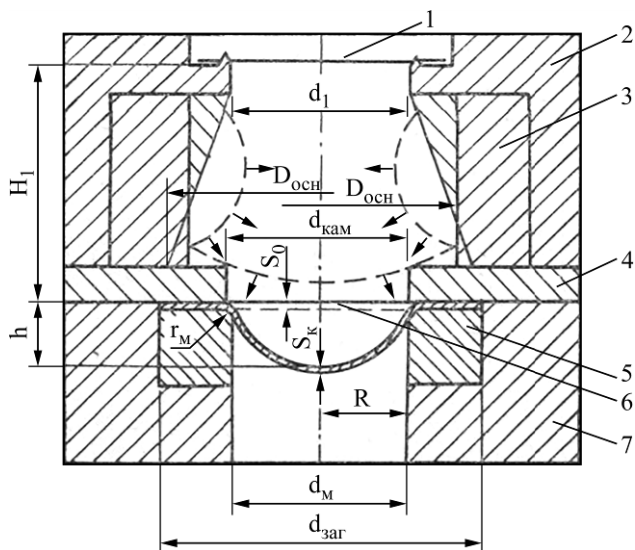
Схема сборки универсальной оснастки [2]. 1 – взрывающаяся проволочка; 2 – разрядная камера; 3 – сменная вставка; 4 – прижимное кольцо; 5 – вытяжное сменное кольцо; 6 – заготовка; 7 – основание матрицы.
